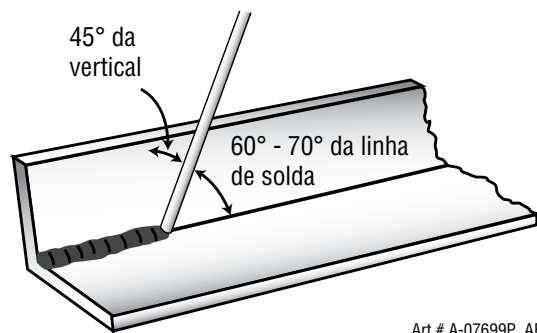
Posição do eletrodo na solda horizontal em ângulo
